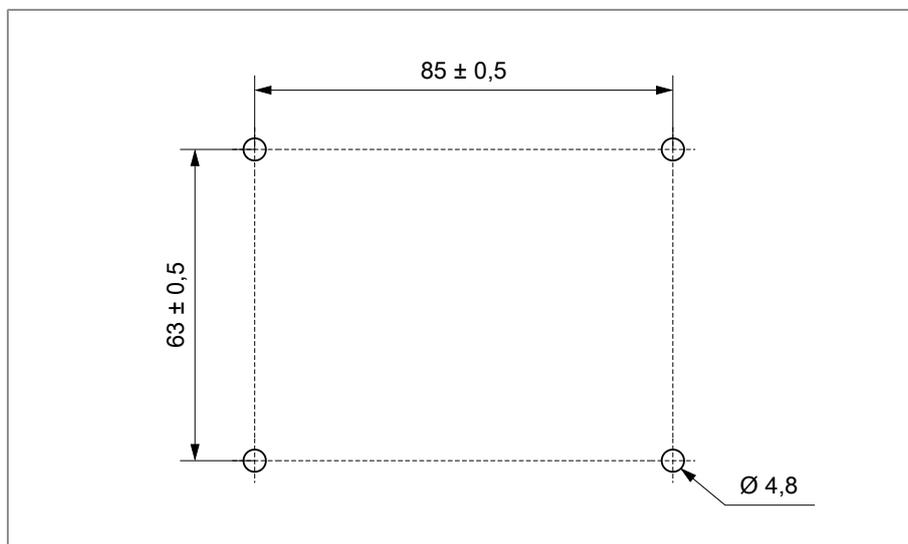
Чертеж с размерами отверстий в крепежной пластине согласующего устройства (мм)
